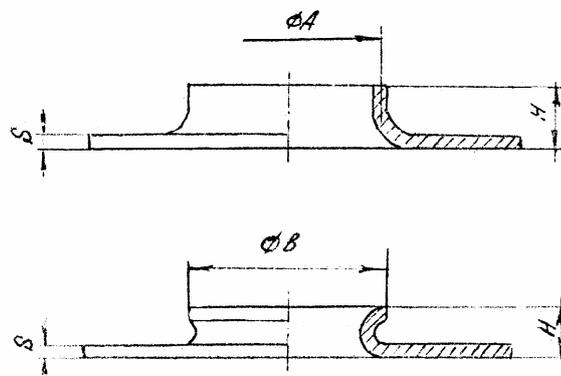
Обозначение размеров элементов разбортованных отверстий.
